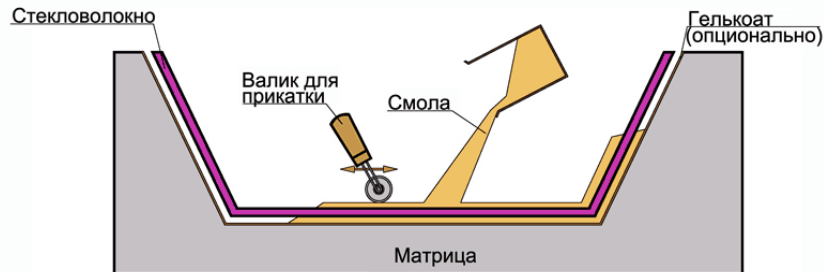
Схема изготовления стеклопластика методом ручного формования.
